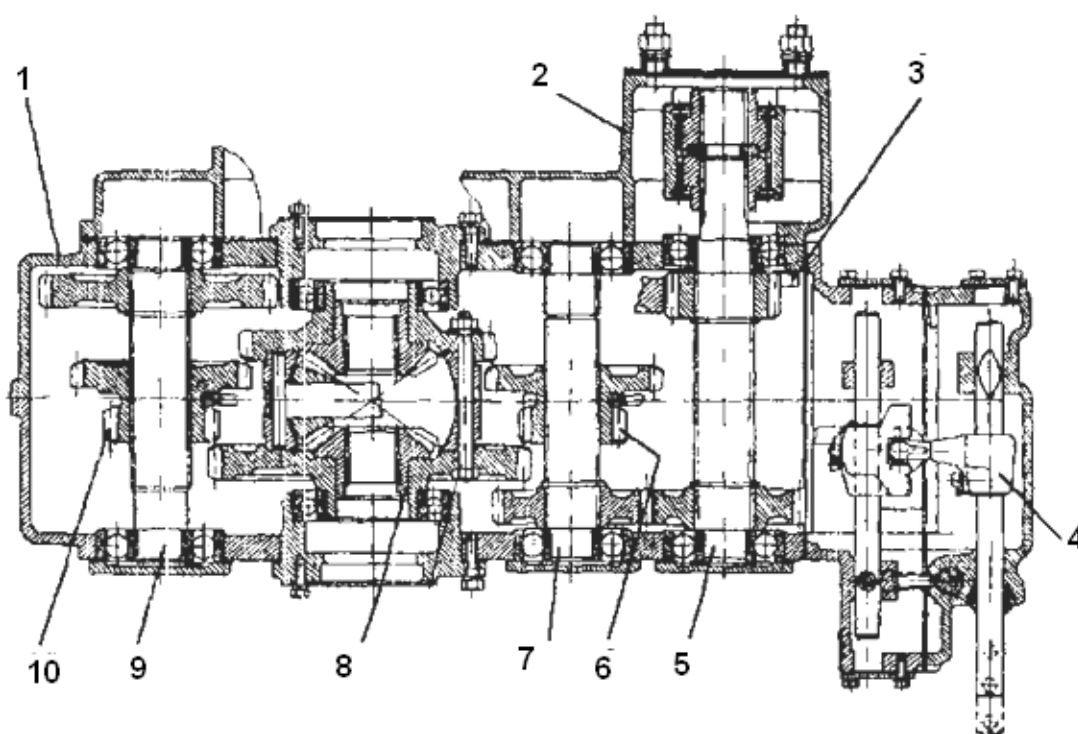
Коробка диапазонов (разрез): 1 – корпус; 2 – корпус установки гидромотора; 3 – болт крепления корпуса гидромотора; 4 – механизм переключения диапазонов; 5 – первичный вал; 6 – блок шестерен, включения третьего и четвертого диапазонов; 7 – нижний промежуточный вал; 8 – дифференциал; 9 – верхний промежуточный вал; 10 – блок шестерен включения первого и второго диапазонов
